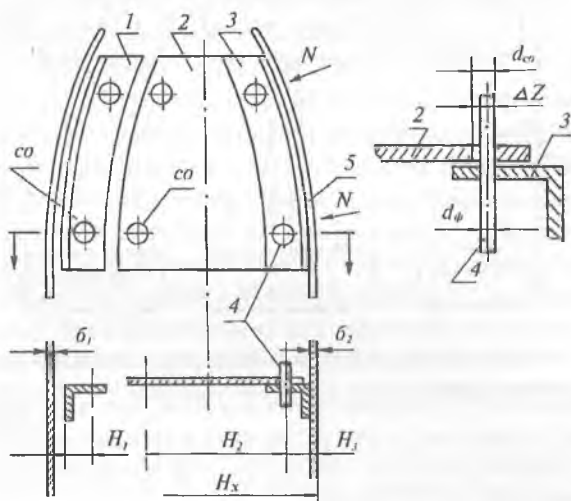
Схема базирования по СО: 1 и 3 — профили; 2 — стенка; 4 — фиксатор (болт); 5 — обшивка
